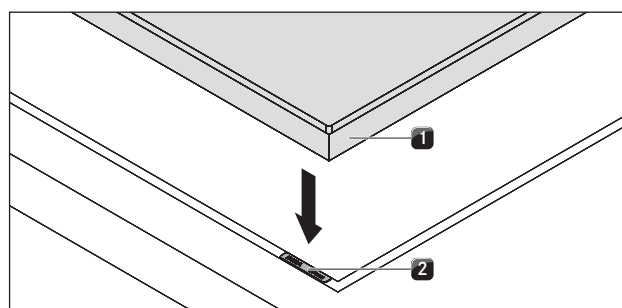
Varná deska umístěná vedle odsavače do varné desky
